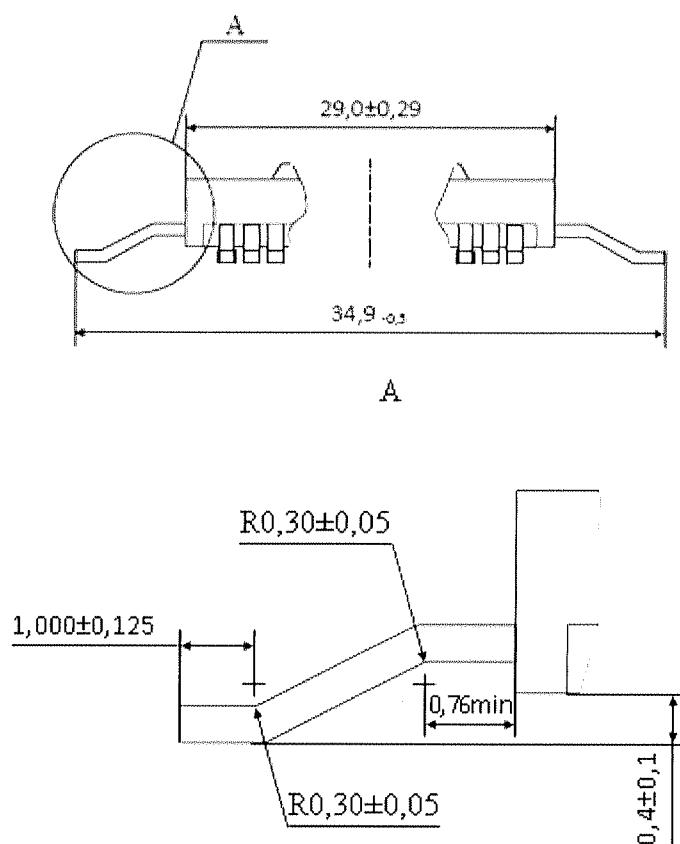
Рекомендуемый вид формовки и обрезки выводов микросхем 5529TP084А
